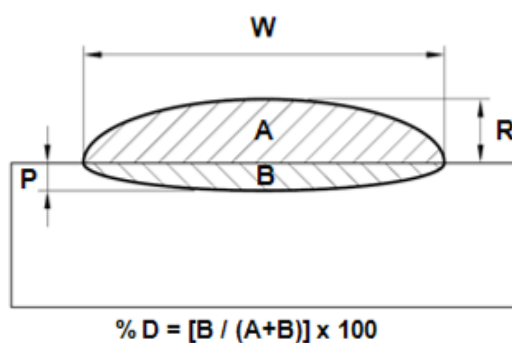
Perfil geométrico desejado do cordão de solda na soldagem de revestimento
